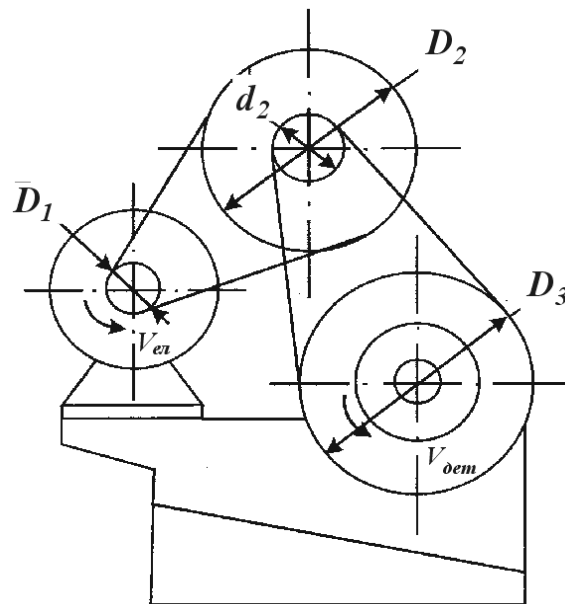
Схема формування обертового руху оброблюваної деталі на верстаті
